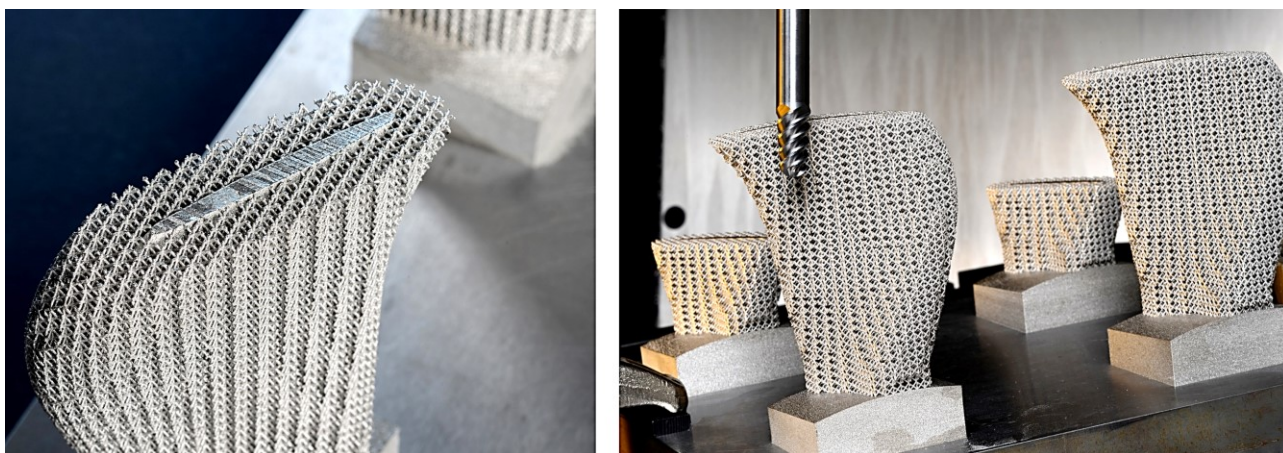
Опорні конструкції виготовлені за допомогою 3D-друку для запобігання вібрації у процесі фінішного фрезерування [29]
